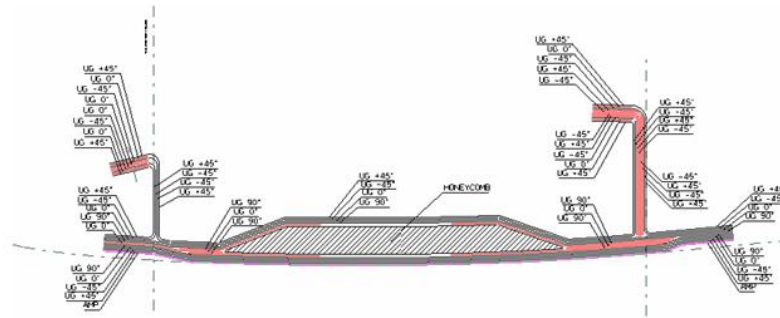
Sezione ala anteriore – elemento inferiore.
